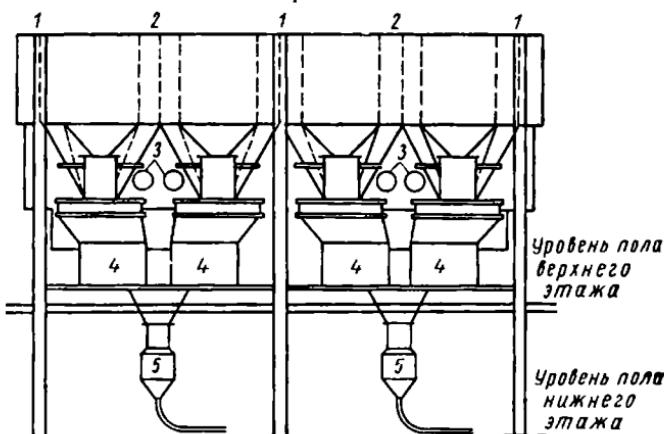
Схема установки с камерным насосом для приготовления стержневых смесей (разрез):
